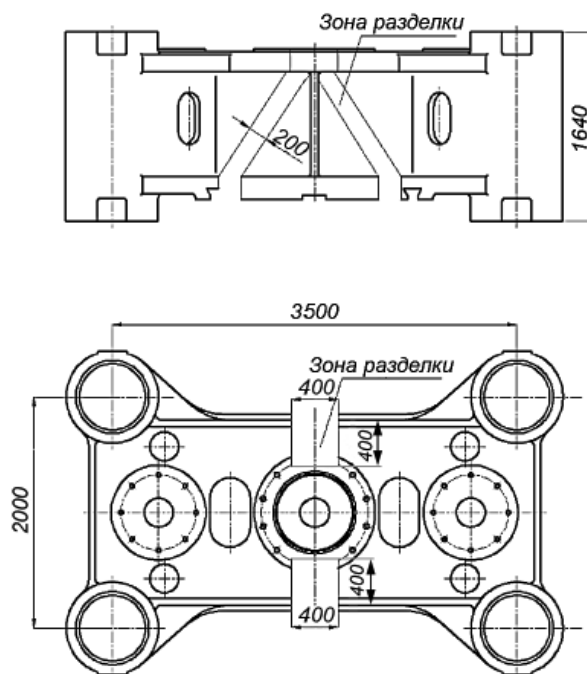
Разделка под сварку боковых стенок, верхней и нижней плит подвижной поперечины ковочного пресса силой 32 МН
